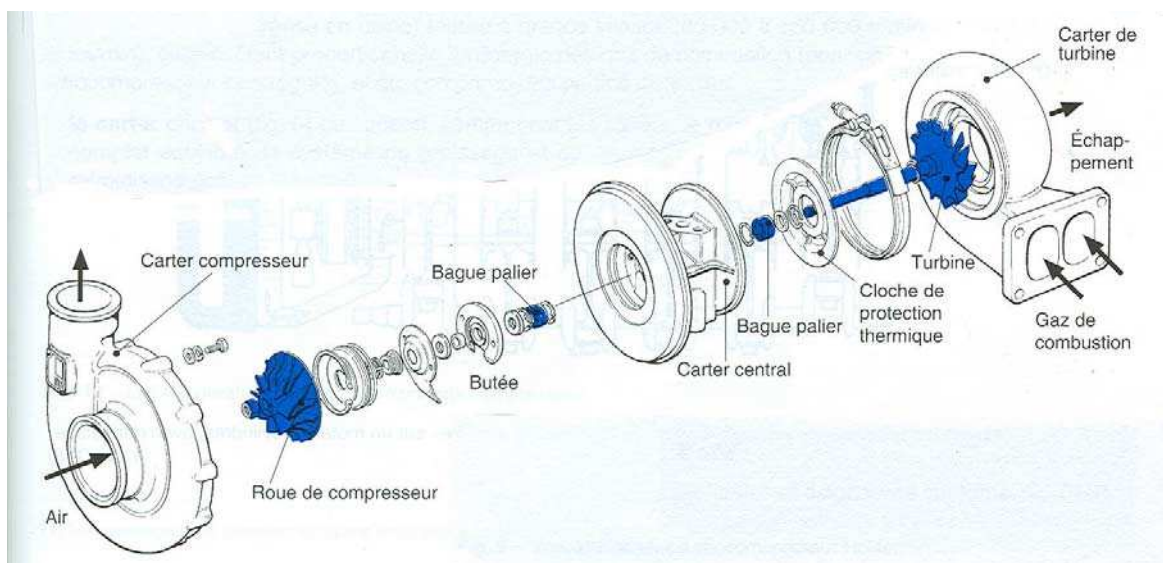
Vue éclatée d'un turbocompresseur HOLSET
